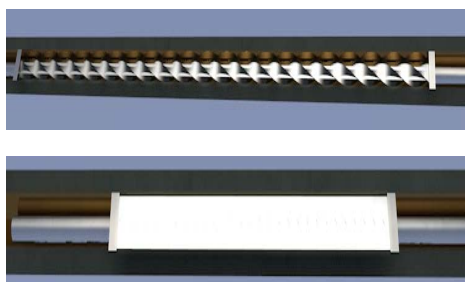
Установка скрученной заготовки в треугольный штамп с последующим прессованием
